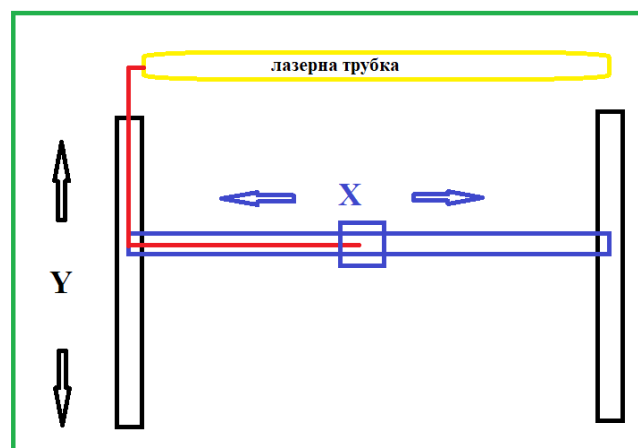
Стандартна компоновка лазерних верстатів з газовою трубкою
